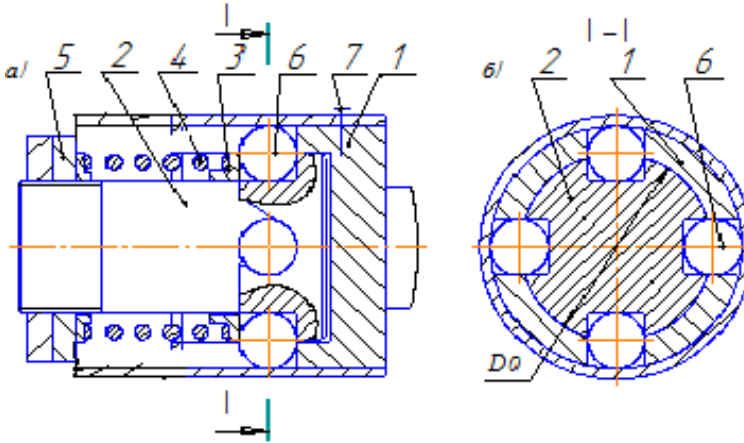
Принципова схема муфти: а) загальний вигляд; б) переріз I-I
